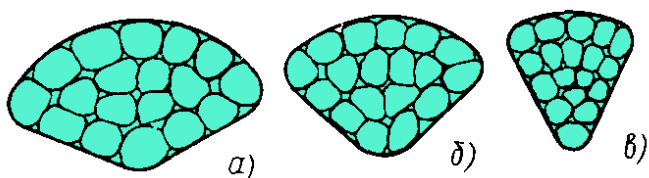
Схема уплотненных секторных токопроводящих жил силовых кабелей: а - трехжильного; б - рабочая жила четырехжильного кабеля; в - нулевая жила четырехжильного кабеля
